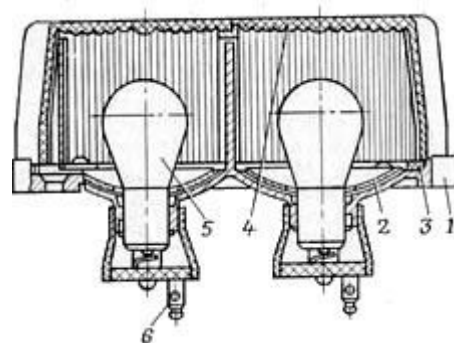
Двухсекционный габаритный фонарь коляски типа ПФ-232:
